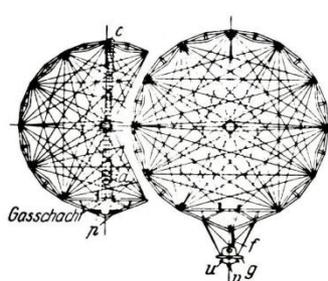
Querschnitt am Hauptring der hinteren Maschinengondel
